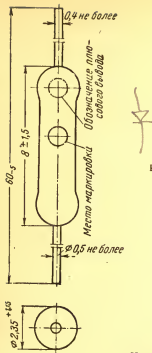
Габаритный чертеж диодов Д9А — Д9М.
